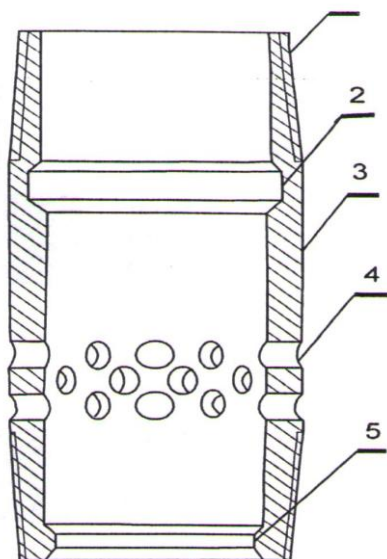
Перфорированный патрубок (усовершенствованный): 1 - резьба 89 (73) мм НКТ; 2 - паз фиксатора замка; 3 - корпус перфорированного патрубка; 4 - калиброванные перфорационные отверстия; 5 - посадочный буртик сбрасываемого иштуцера
